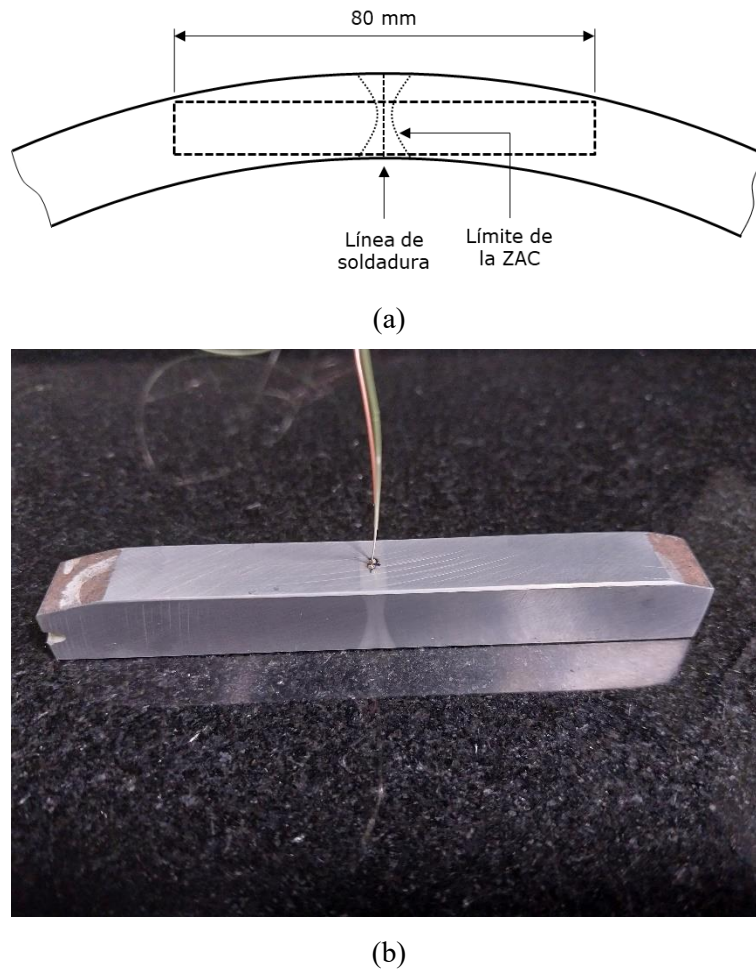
(a) Esquema de la posición de la probeta prismática respecto de la soldadura. (b) Vista de la probeta con la termocupla soldada (atacada con Nital para revelar la posición de la soldadura).
